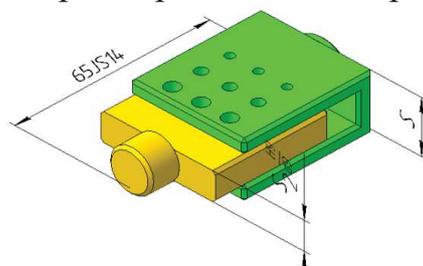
Общий вид приспособления для проведения испытаний заклепочных соединений
